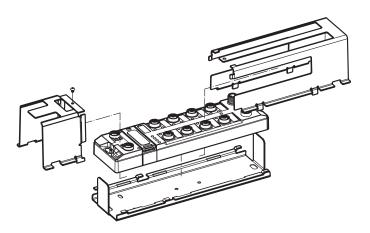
Montaggio del dispositivo nell'involucro protettivo TB-SG-L
